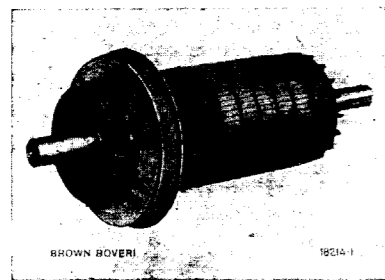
ª—Rotor de un motor de arranque centrífugo, tipo M E.
